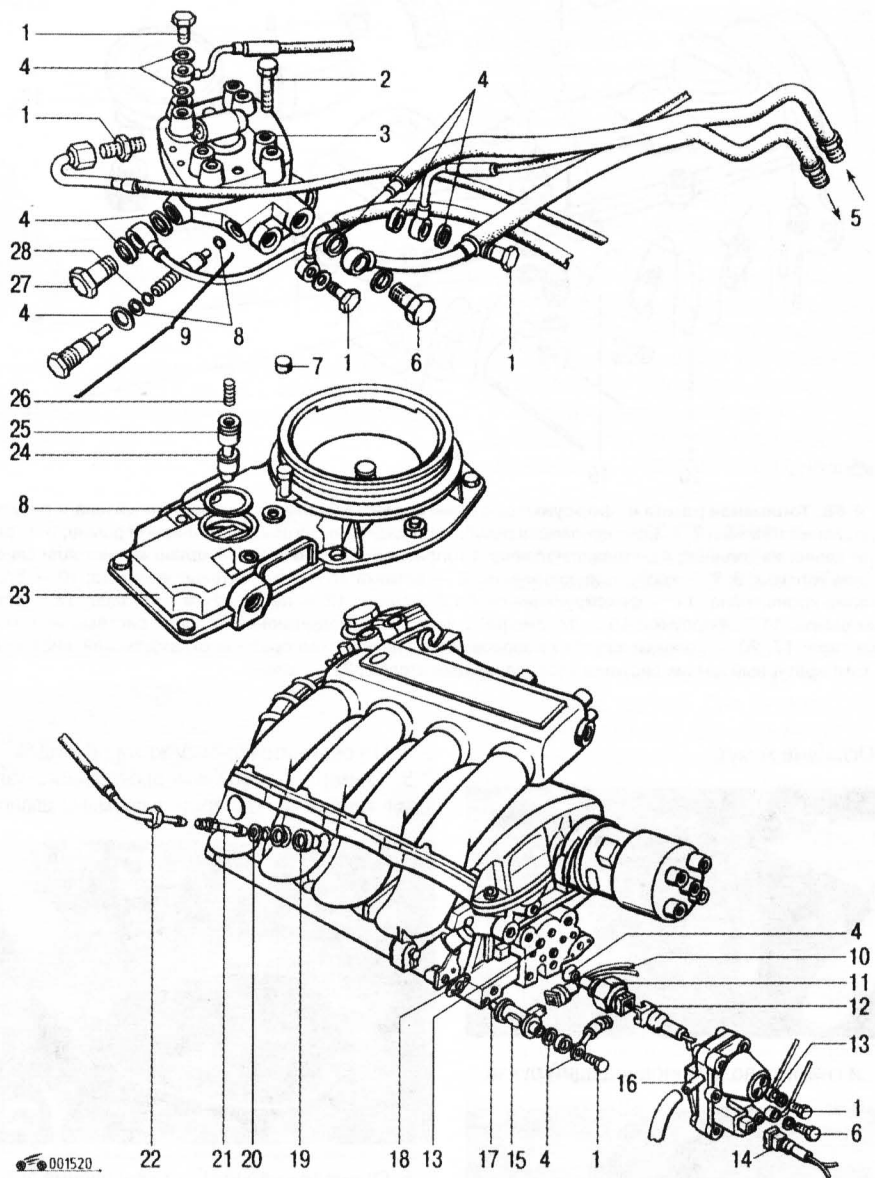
Элементы системы впрыска топлива K-Jetronic: 1 - болт; 2 - винт; 3 - распределитель топлива; 4, 8, 20 - уплотнительные кольца; 5 - топливные шланги; 6, 27 - пустотелый болт; 7 - заглушка; 9 - регулятор давления; 10 - колодка жгута проводов (синего цвета); 11 - выключатель пусковой подачи топлива; 12 - колодка жгута проводов (коричневого цвета); 13 - датчик температуры; 14 - колодка жгута проводов (серого цвета); 15 - нагреватель; 16 - вакуумный штуцер; 17 - клапан холодного пуска; 18 - прокладка; 19 - втулка; 21 - форсунка; 22 - вакуумный магистральный; 23 - измеритель расхода воздуха; 24 - плунжер; 25 - винт регулировки содержания СО; 26 - пружина; 28 - регулировочная шайба
